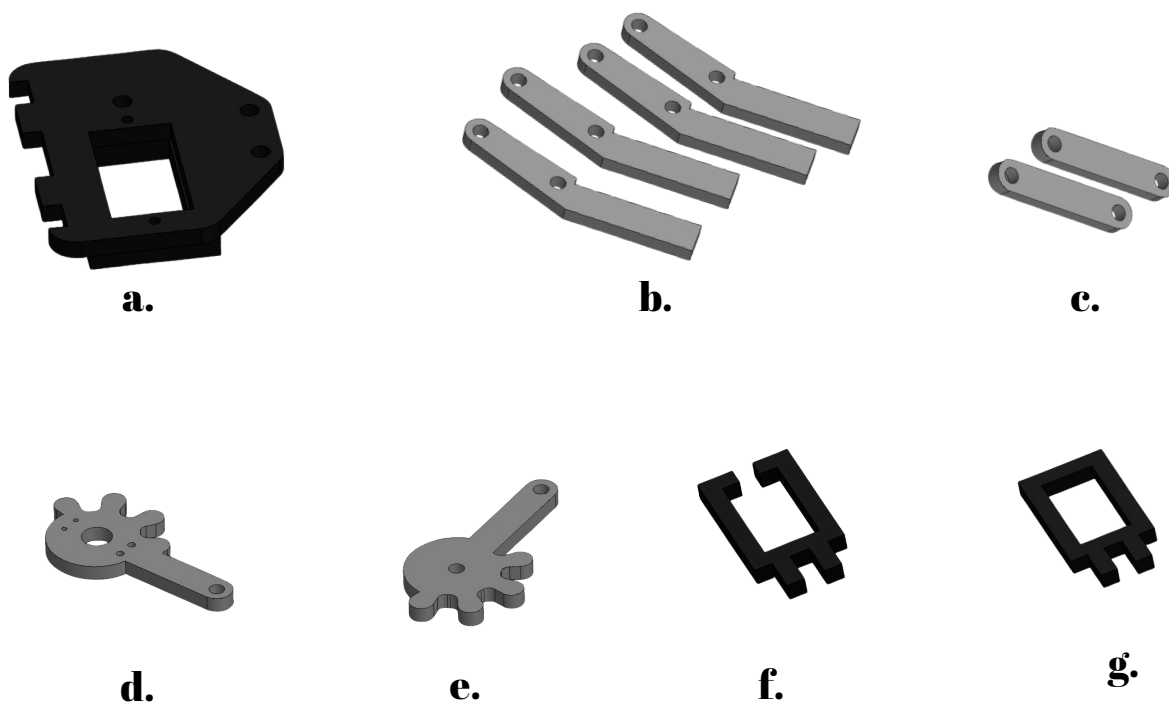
a. Base garra. b. soportes laterales. c. Pieza de unión. d. engranaje derecho. e. engranaje izquierdo. f. sujetador de servo 1. g. sujetador de servo 2.
